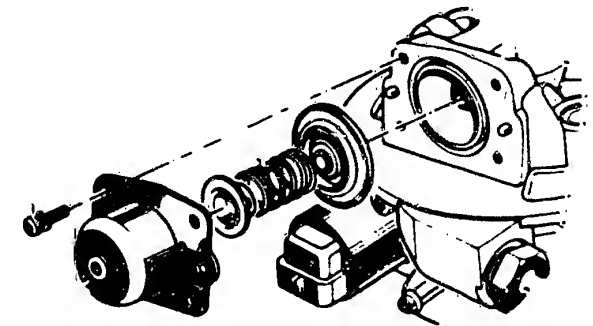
Beim Einbau des Druckreglers ist zu beachten, dass die Membrane richtig in der Nut des Gehäuses sitzt.
